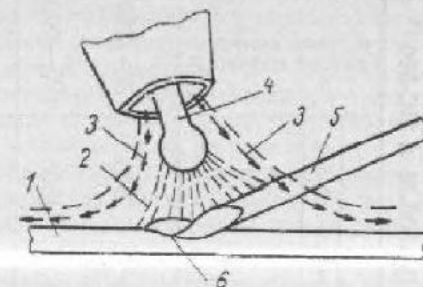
Схема дуговой сварки в среде защитного газа.
